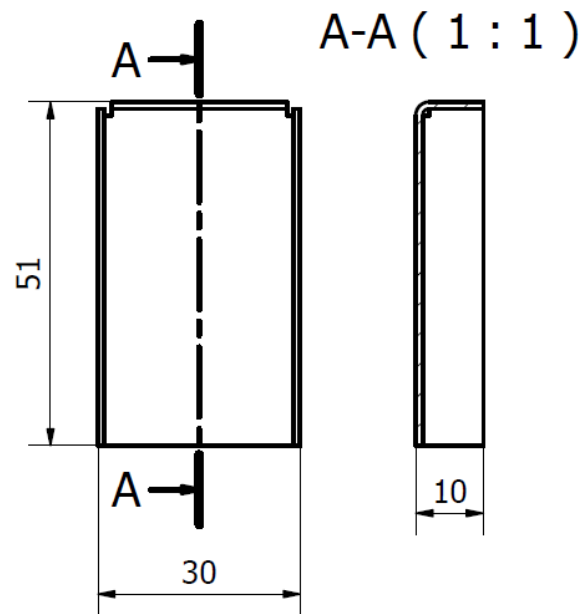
Exemplo de desenho 2D de uma chapa quinada
